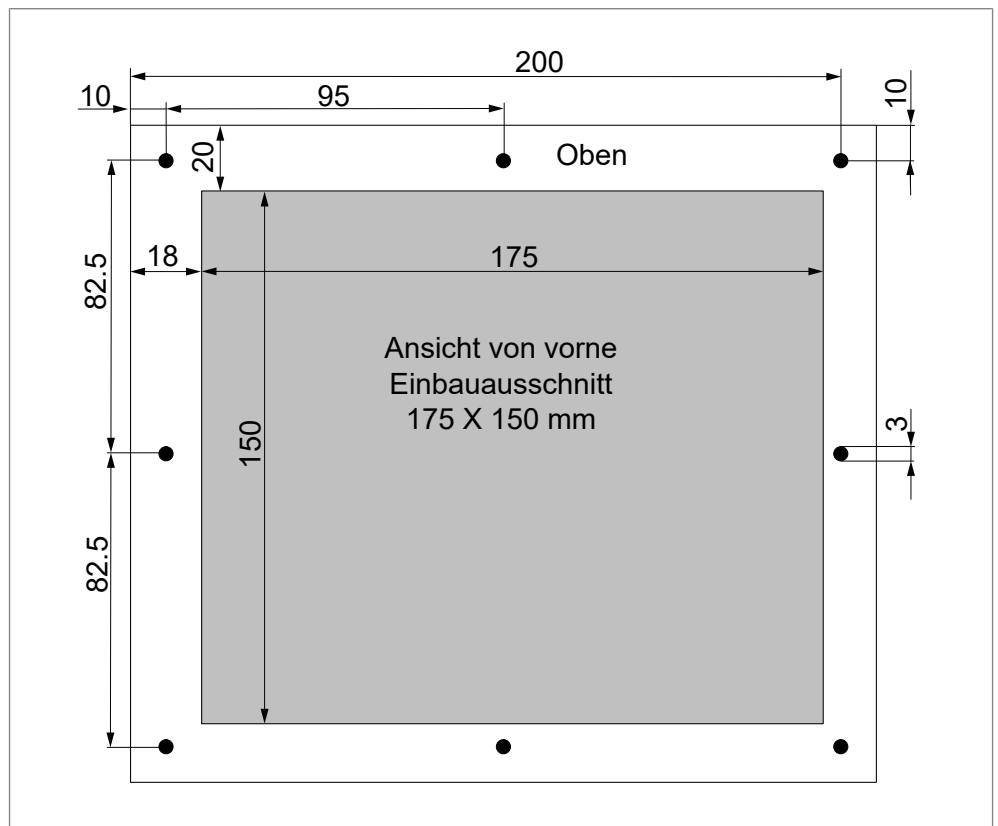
Bohrbild Einbaugehäuse (Ansicht Rückseite)
